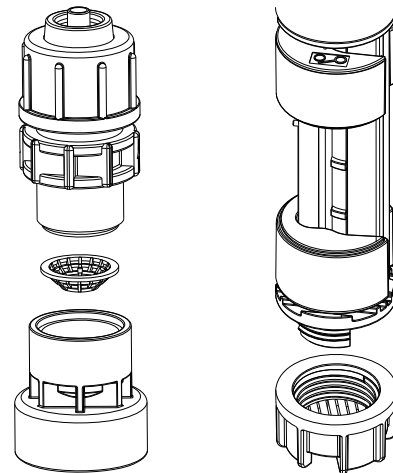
Fußventil (links), Sauglanze (rechts): Sieb entfernen
